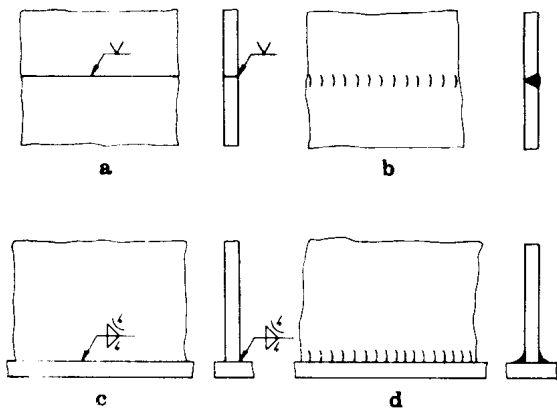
图示形式 a. 对接焊缝代号; b. 对接焊缝说明图; c. 双角焊缝代号; d. 双角焊缝说明图
